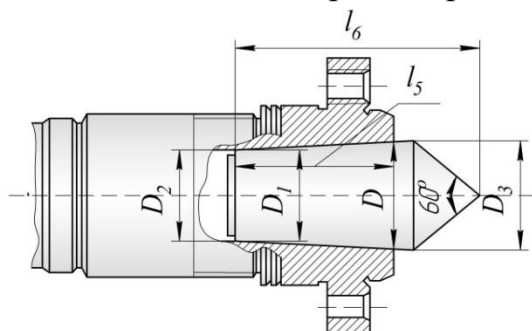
Эскиз конца шпинделя станка с упорным центром
